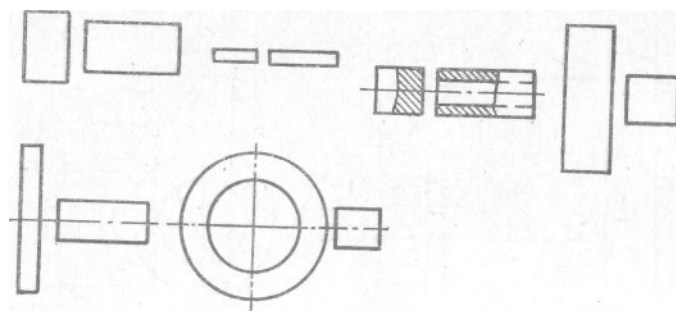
Типы сварных соединений стыковой сварки оплавлением
